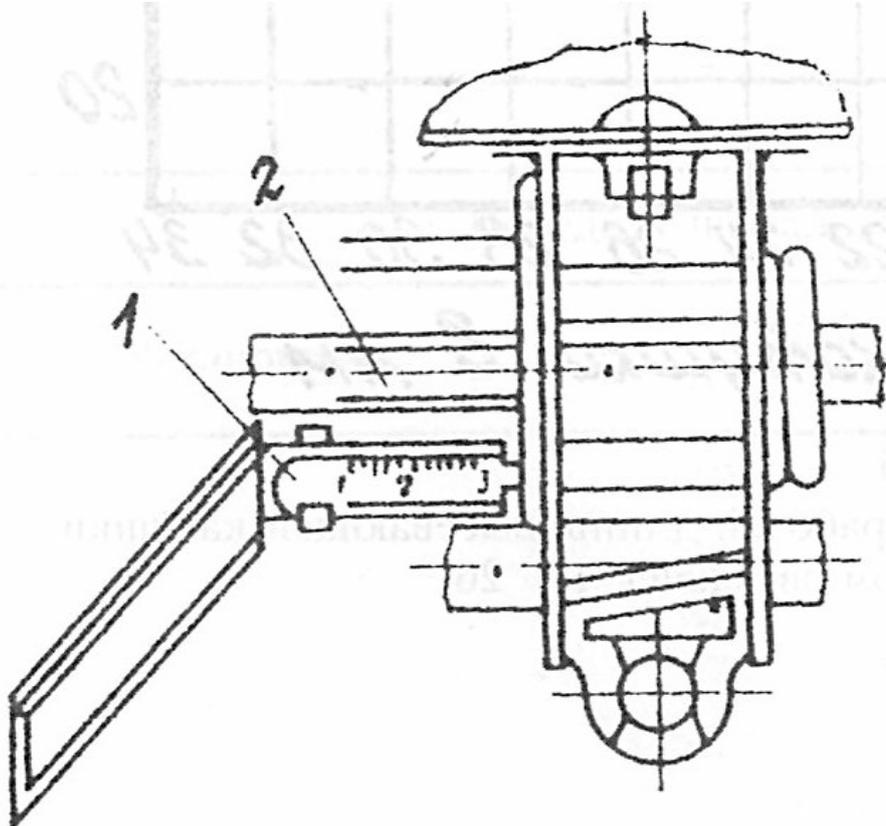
Проверка рабочей длины катушки зерновых сеялок:
